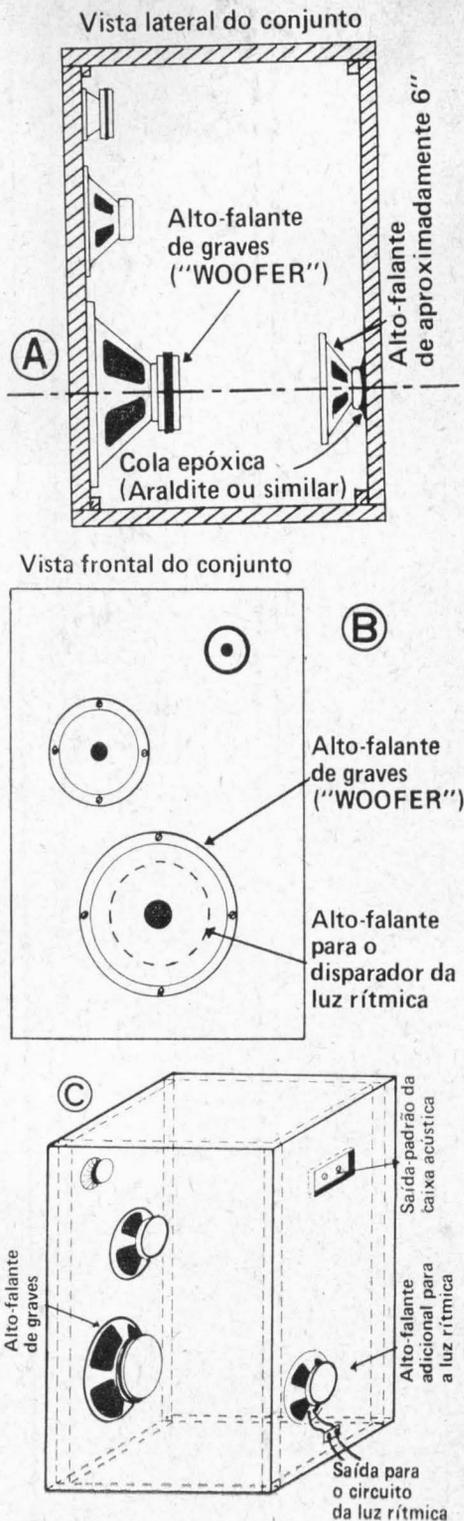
a) Vista lateral do conjunto; b) Vista frontal do conjunto; c) Vista em perspectiva.
